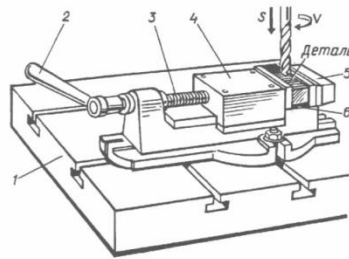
Схема кріплення деталі у верстатних гвинтових лещатах: 1 – стіл; 2 – рукоятка; 3 – гвинт; 4 – рухома губка; 5 – нерухома губка; 6 – планка
